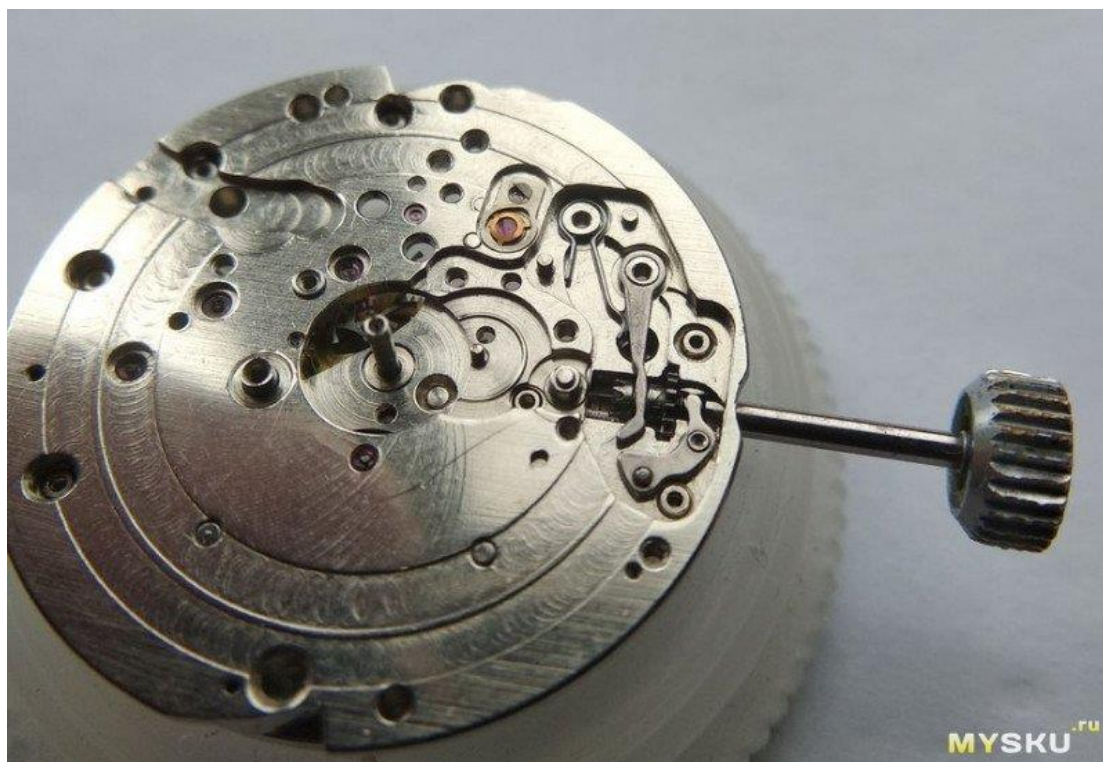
Механізм годинника виготовлений за допомогою верстату з ЧПК, фрезером
